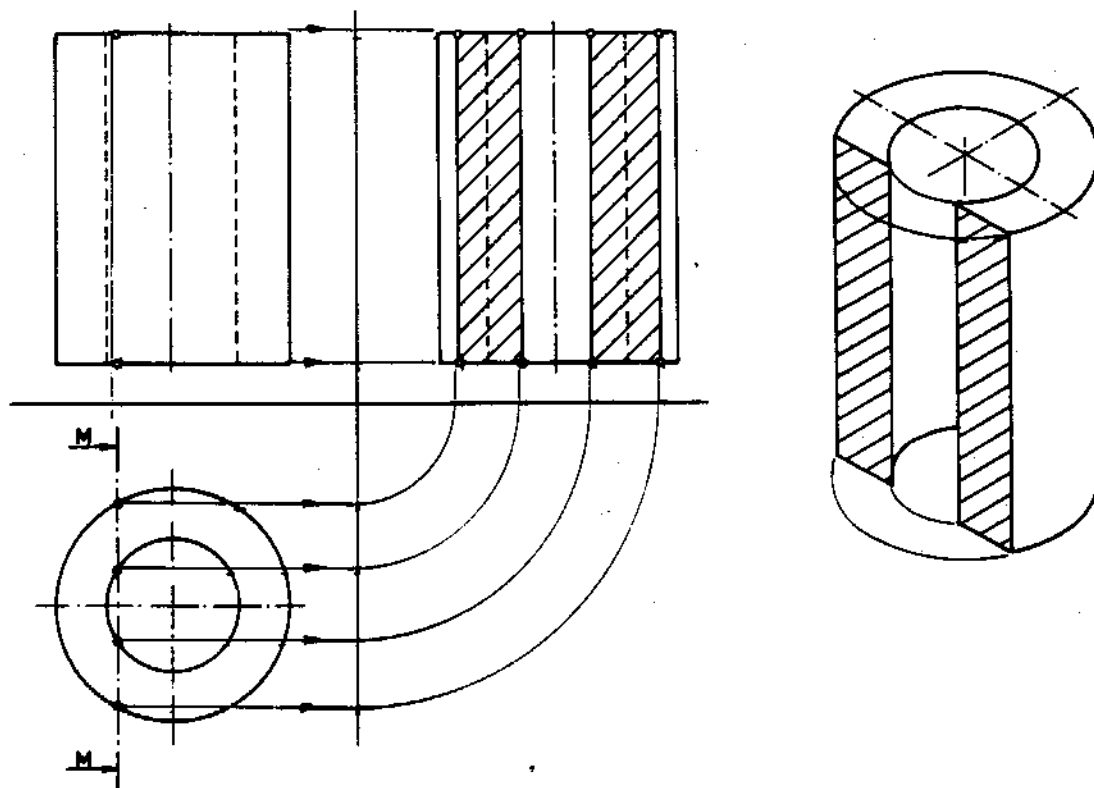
Sezione di un cilindro cavo mediante un piano di traccia MM. parallelo all'asse del solido.
